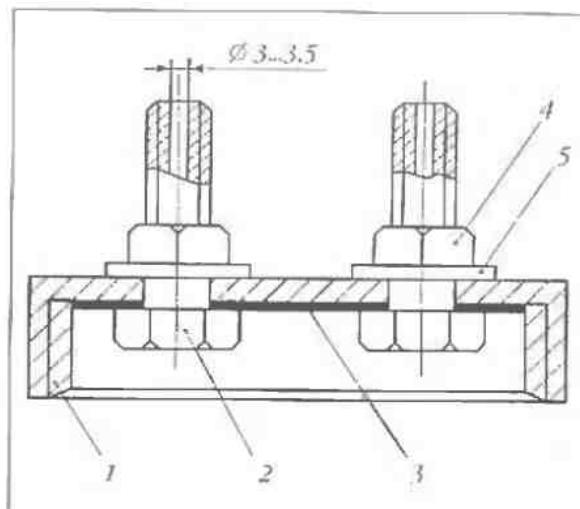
Схема крышки ресивера с входным и выходным патрубками, выполненнымными из болтов М8: 1 – крышка; 2 – база; 3 – прокладка из листовой резины; 4 – гайка; 5 – шайба
